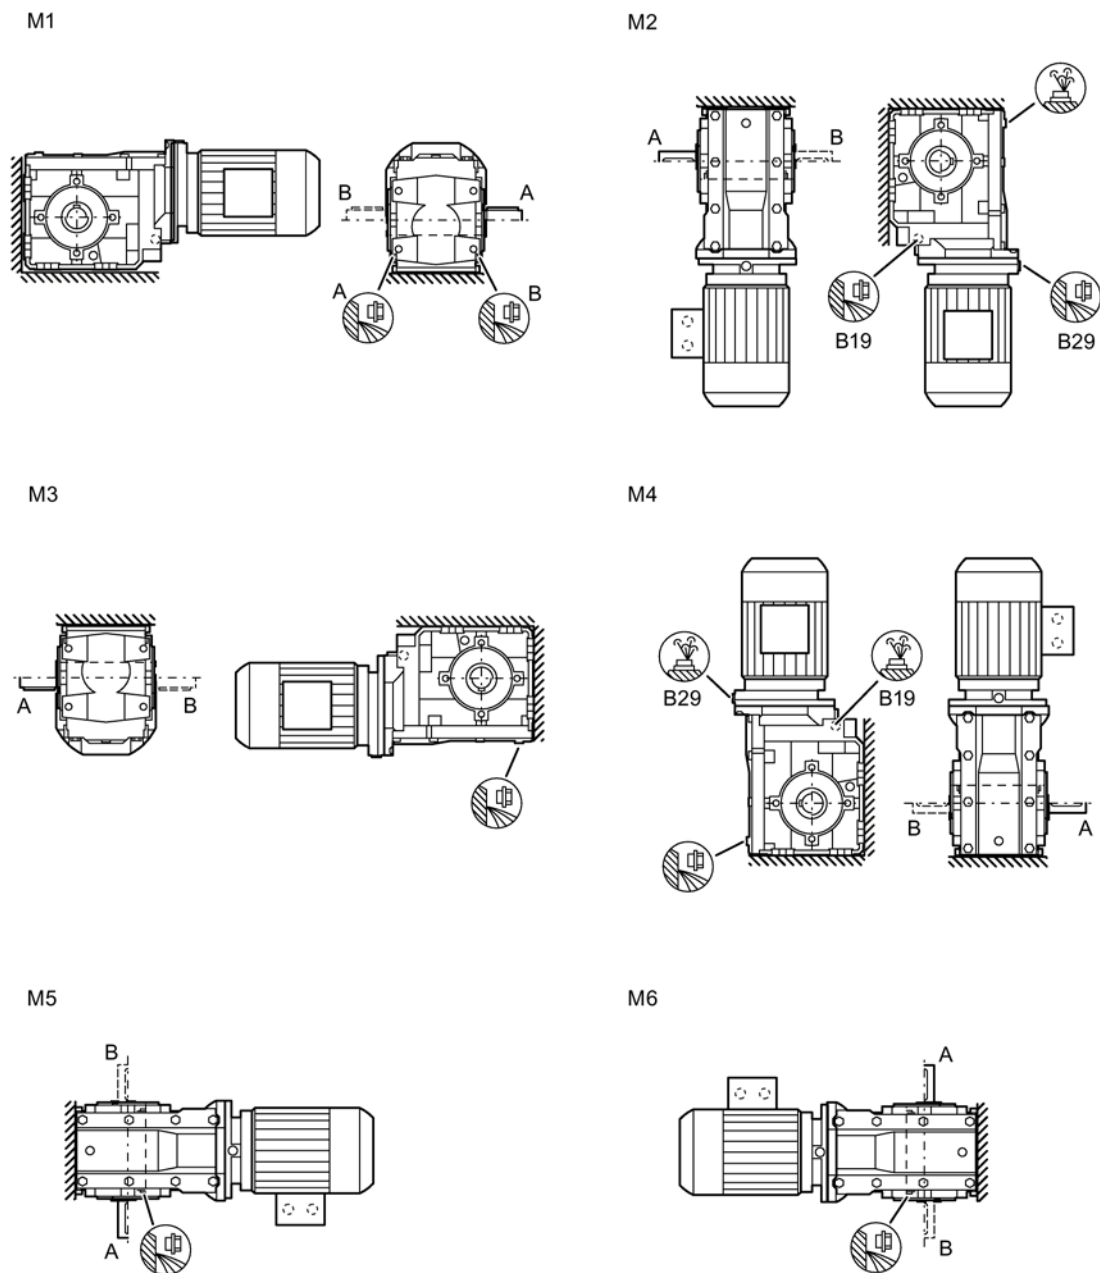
Монтажные положения для конического редуктора В. в исполнении на лапах, типоразмеры 19–29
